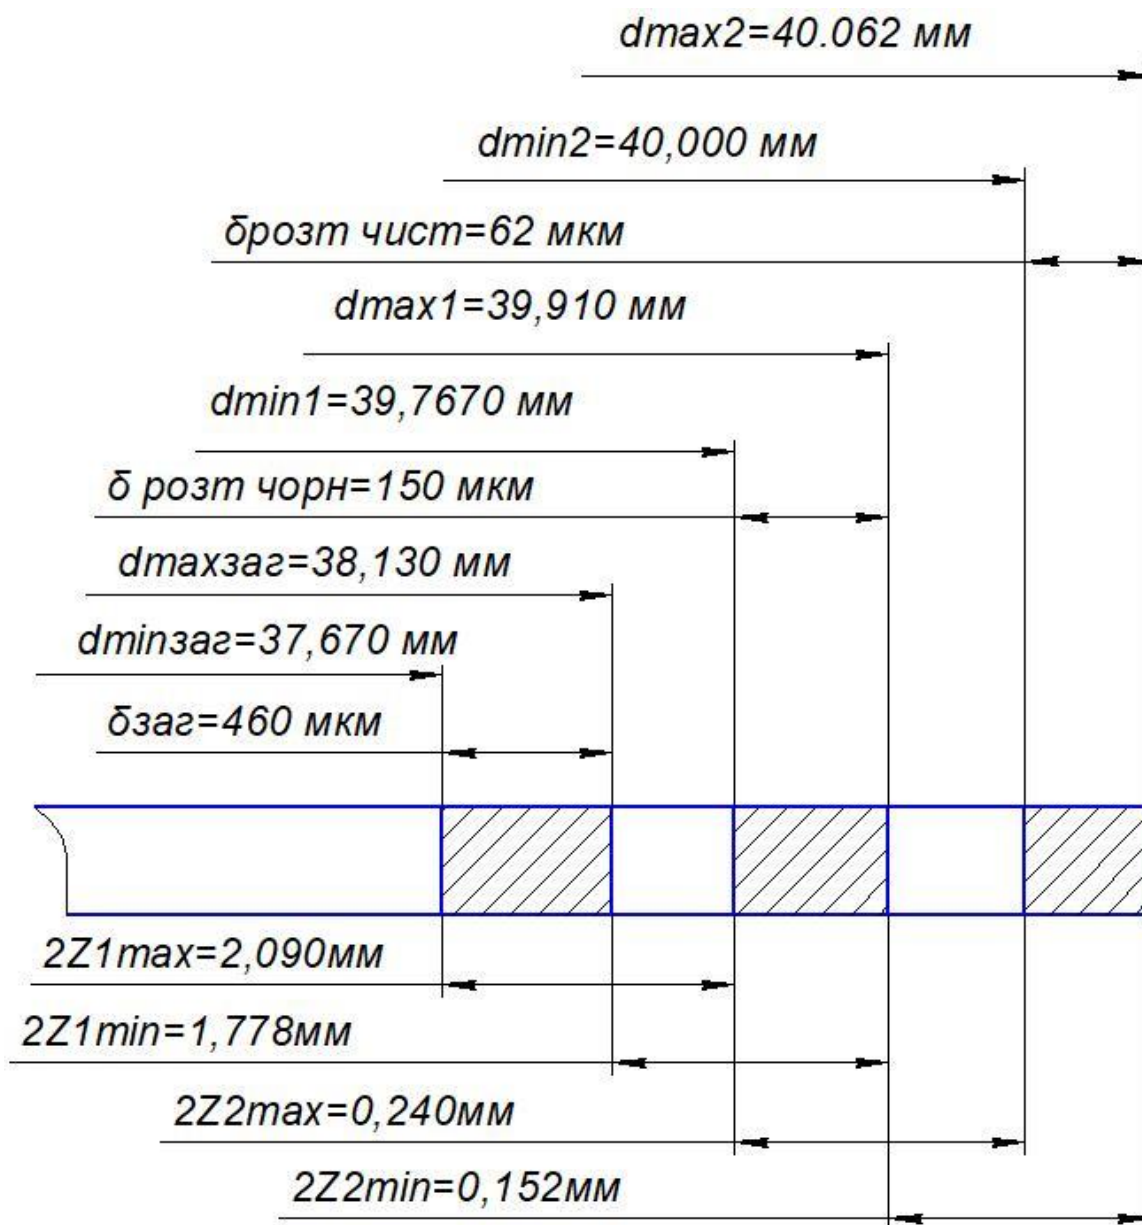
Схема графічного розміщення припусків та допусків на обробку поверхні  $\varnothing 40(H9)^{+0.062} ..$
